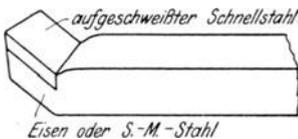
Aufschweißen auf Eisen oder S.-M.-Stahl.
